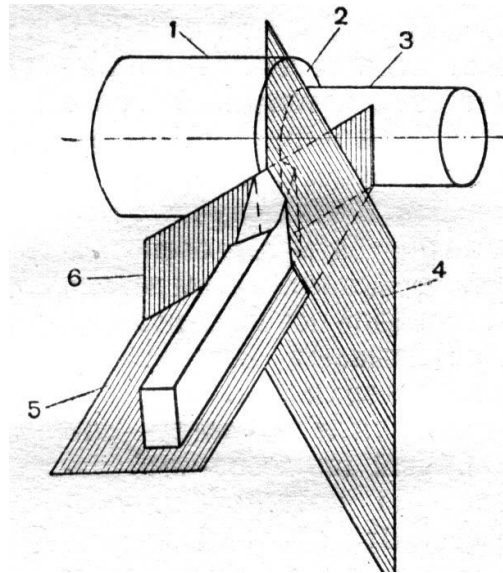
Поверхні і площини при обробці деталей на токарному верстаті
